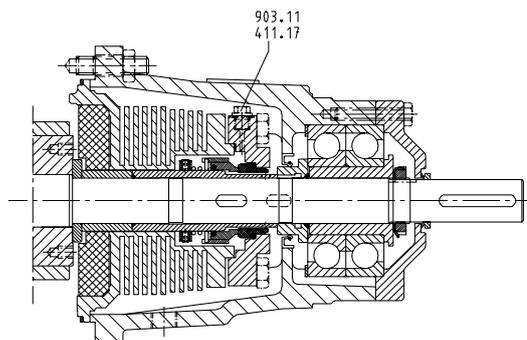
Пробка выпуска воздуха из камеры уплотнения (корпус уплотнения с воздушным охлаждением) — типоразмеры 32–100
